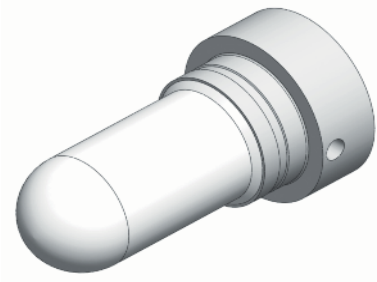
Чашечный диффузор из сплава Хастеллой в сборе
